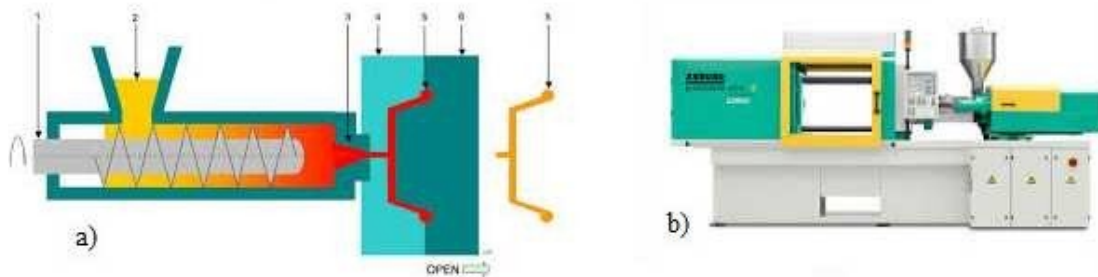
Machine d'injection(a) schéma de la machine, [16] b) photo d'une machine d'injection) [17]
